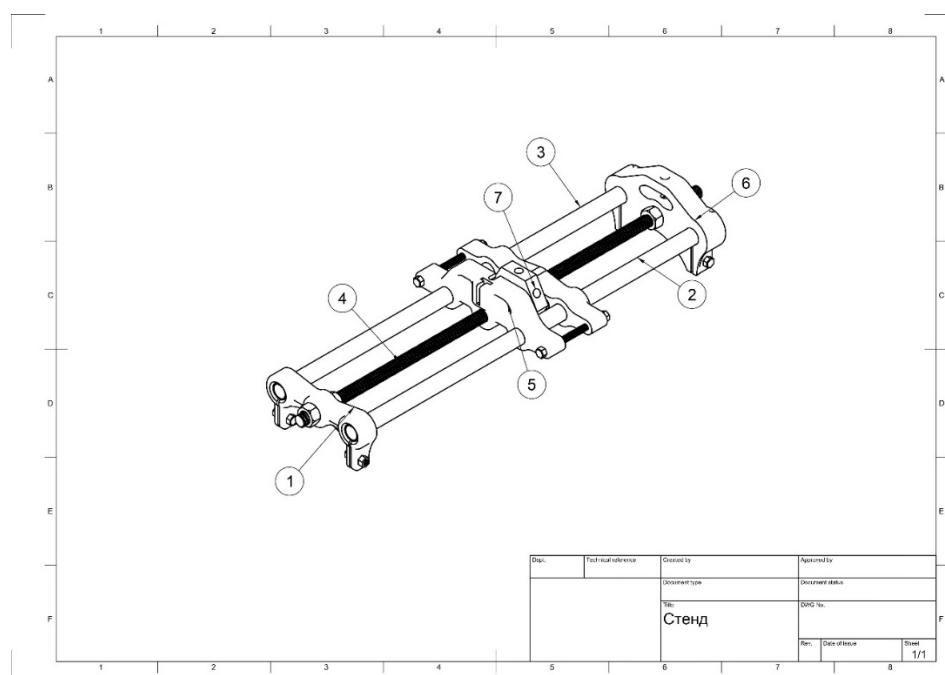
Сборочный чертёж стенда: 1 – стойка; 2, 3 – направляющие; 4 – шпилька; 5 – каретка; 6 – стойка с креплением под измерительный прибор; 7 – колесо
